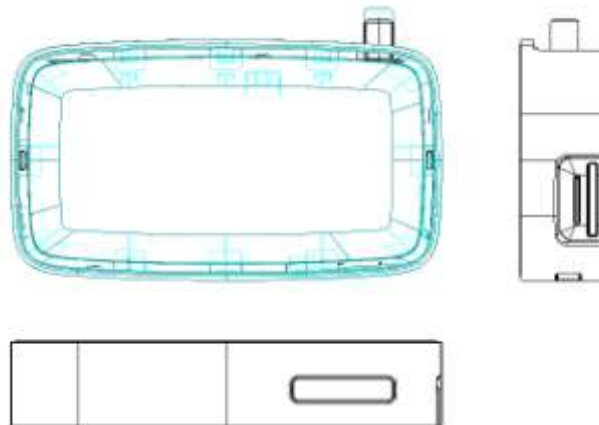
：比對原始設計尺寸 2D-CAD 示意圖
